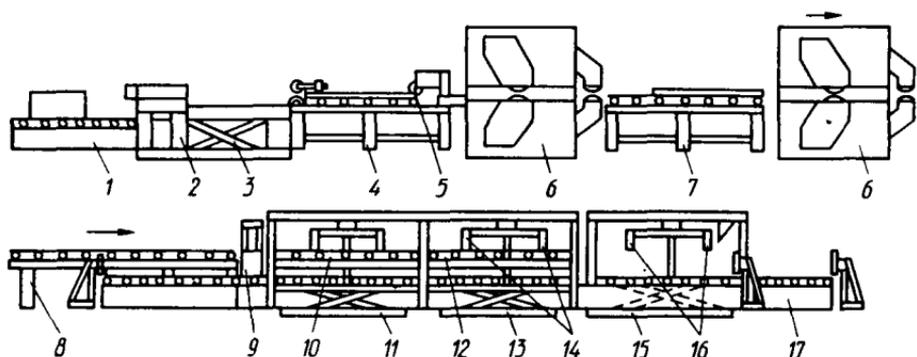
Схема автоматической линии шлифования ДЛШ50М:
